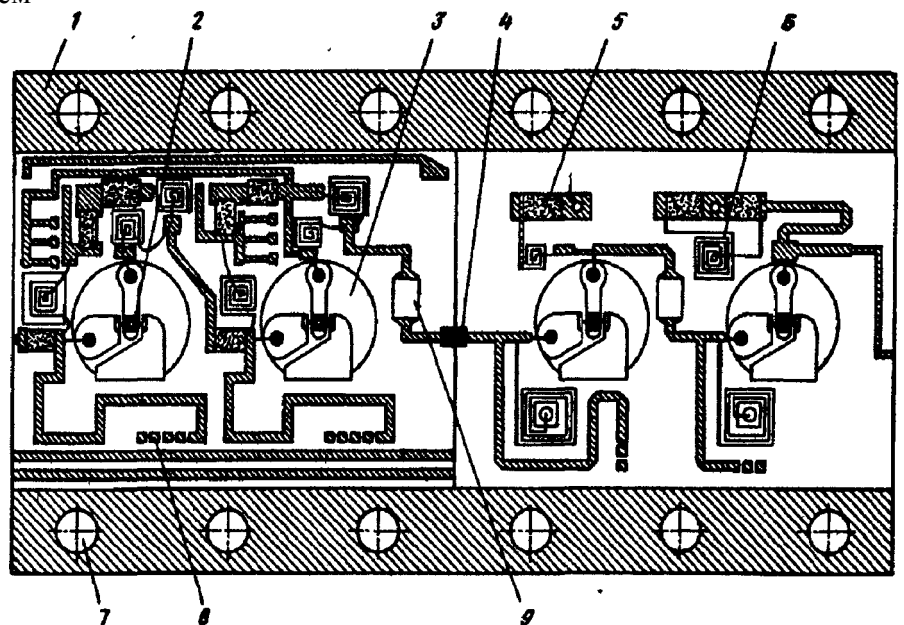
Конструкция передающего СВЧ-модуля: 1 — металлическое основание, 2 — мощный СВЧ-транзистор; 3 — брокеритовая вставка (шайба); 4 — фольговая перемычка; 5 — конденсатор; 6 — пленочная катушка индуктивности, 7 — отверстие для крепления; 8 — шлейф для подстройки; 9 — навесной ЭРЭ
